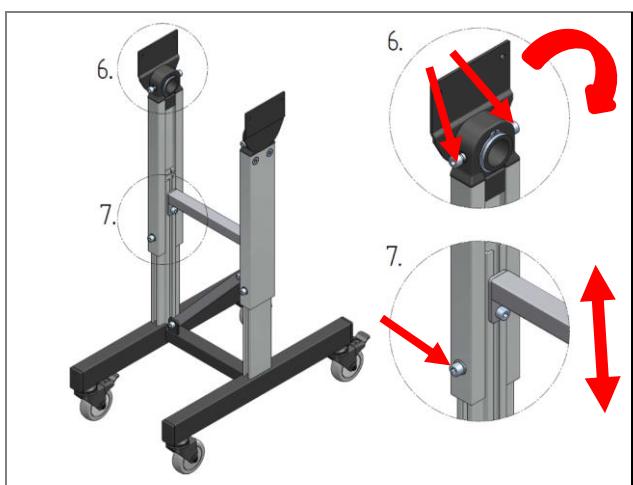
HE 050 / HM 480 alt şasisinin montajı
